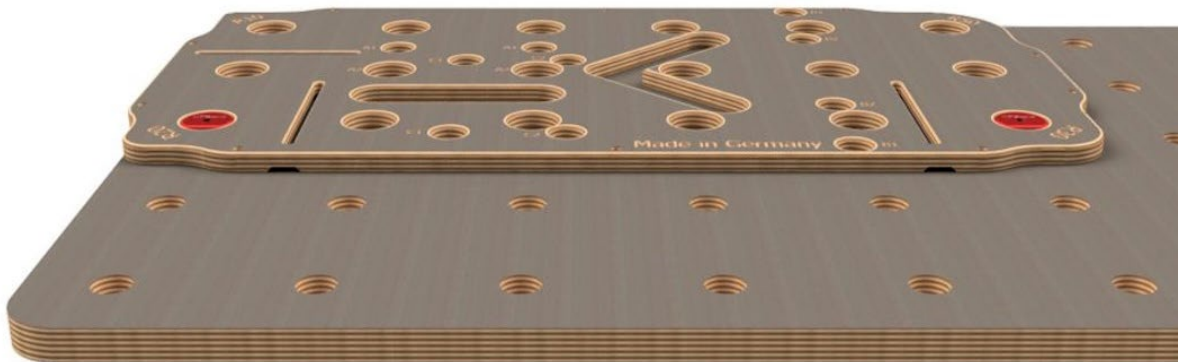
Bench Dogs insatta i mallen och arbetsstycket
